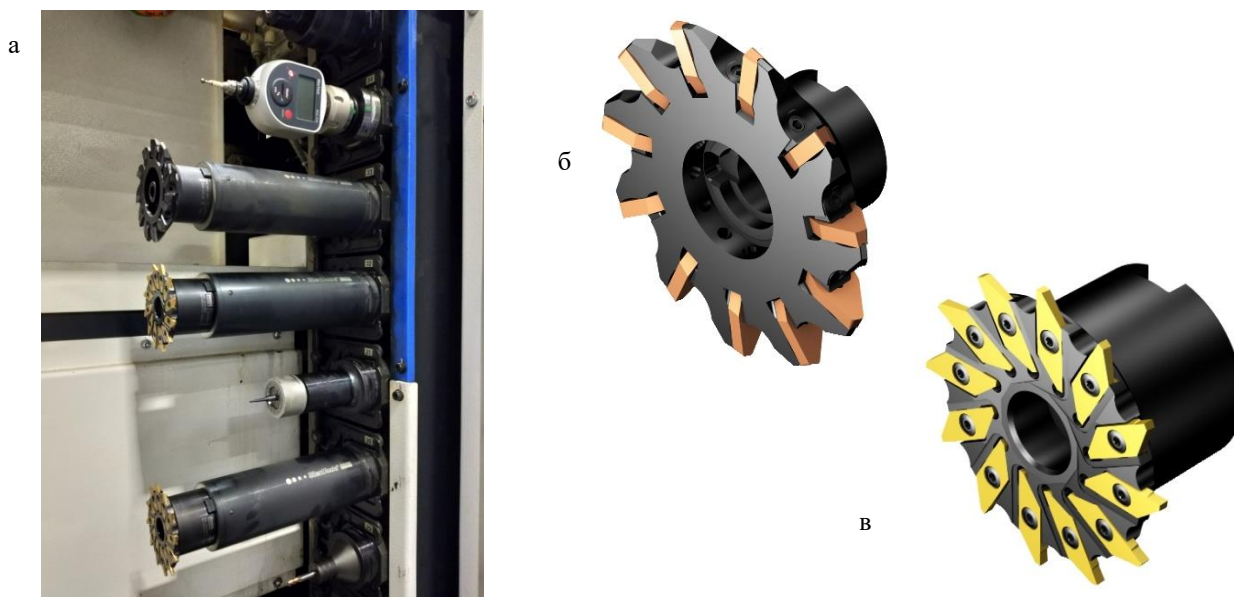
Дисковые фрезы производства Sandvik Coromant для обработки впадин зубьев: а – установленные в инструментальном магазине станка Integrex I300S фирмы «Mazak»; б – фреза Coromill 162; в – фреза Coromill 161
